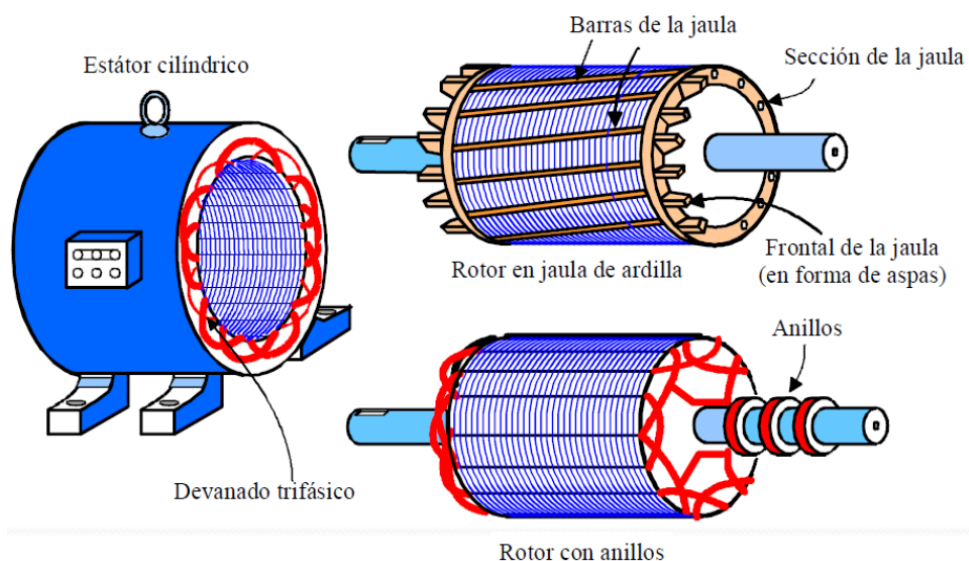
Elementos principales que componen al motor de inducción. Fuente: [24].
